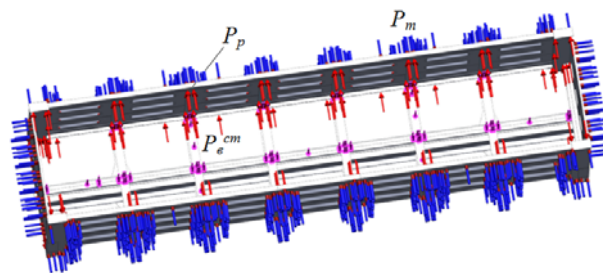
Розрахункова схема несучої конструкції напіввагона
